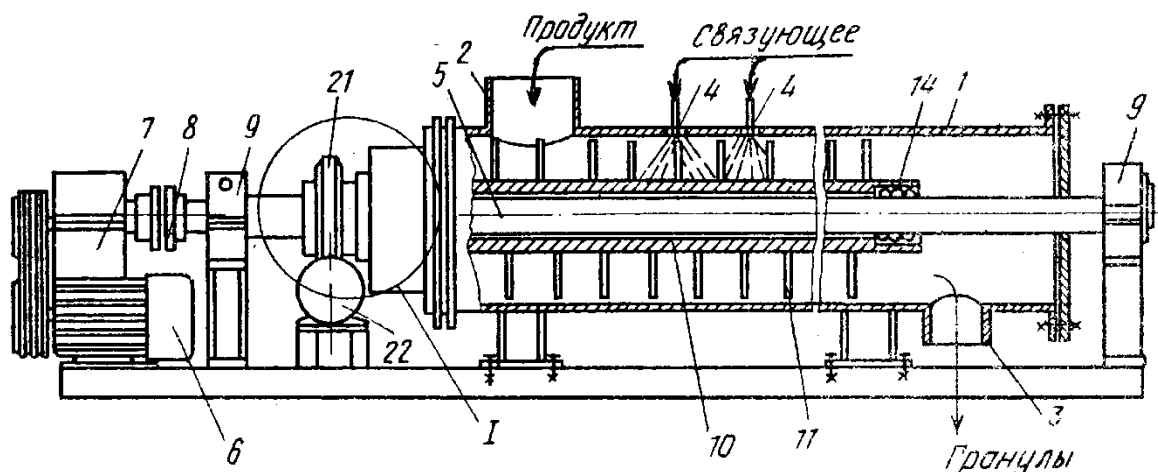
Гранулятор сыпучих материалов: 1 – цилиндрический корпус; 2 – штуцер для загрузки продукта; 3 – штуцер для разгрузки продукта; 4 – форсунки; 5 – центральный вал; 6 – электродвигатель; 7 – редуктор; 8 – муфта; 9 – подшипниковые узлы; 10 – полый вал; 11 – штифты; 12, 13 – продольные канавки; 14 – шарики; 15 – упорный подшипник; 16 – втулка; 17 – палец; 18 – паз; 19 – втулка; 20 – подшипник; 21 – червячное колесо; 22 – реверсивный электродвигатель; 23 – червяк
